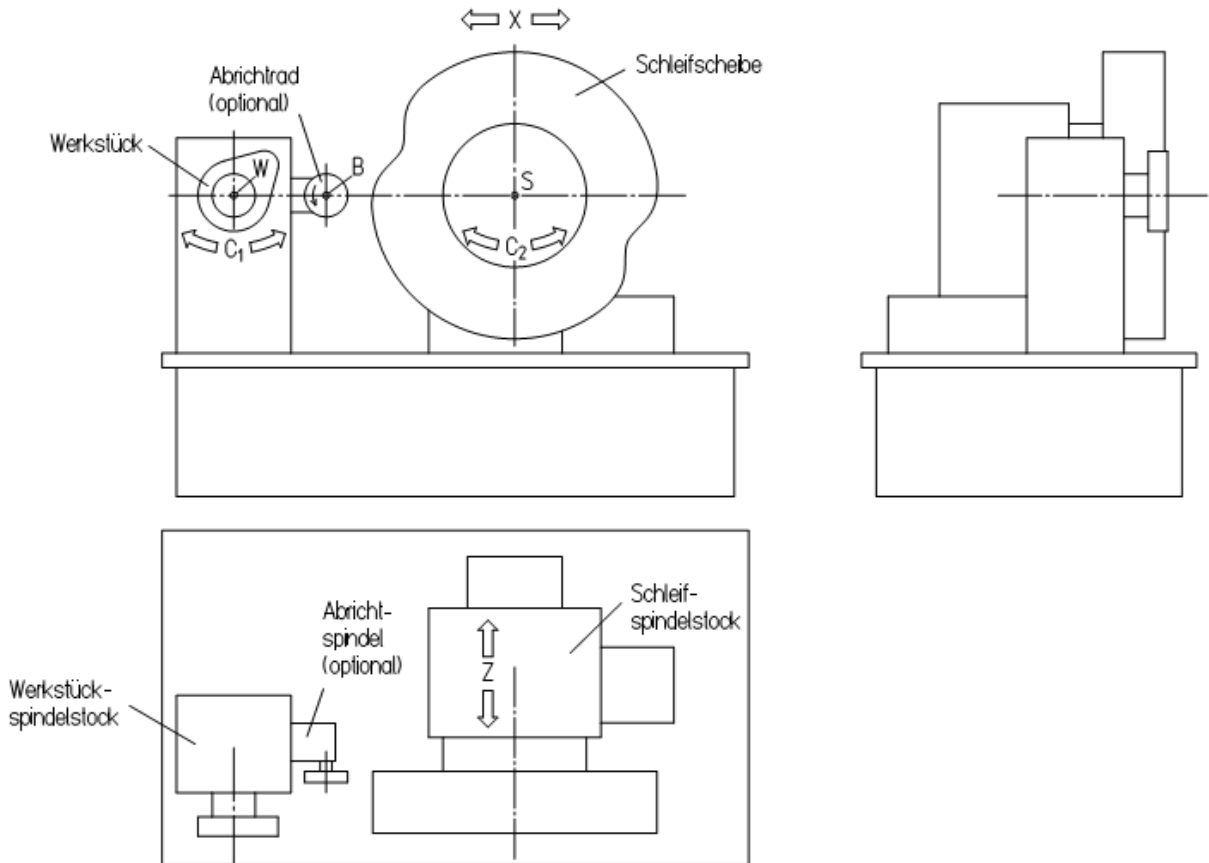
Unrundschleifmaschine zum Nockenschleifen mit zwei Drehachsen, zwei Linearachsen und einer optionalen Abrichtspindel
